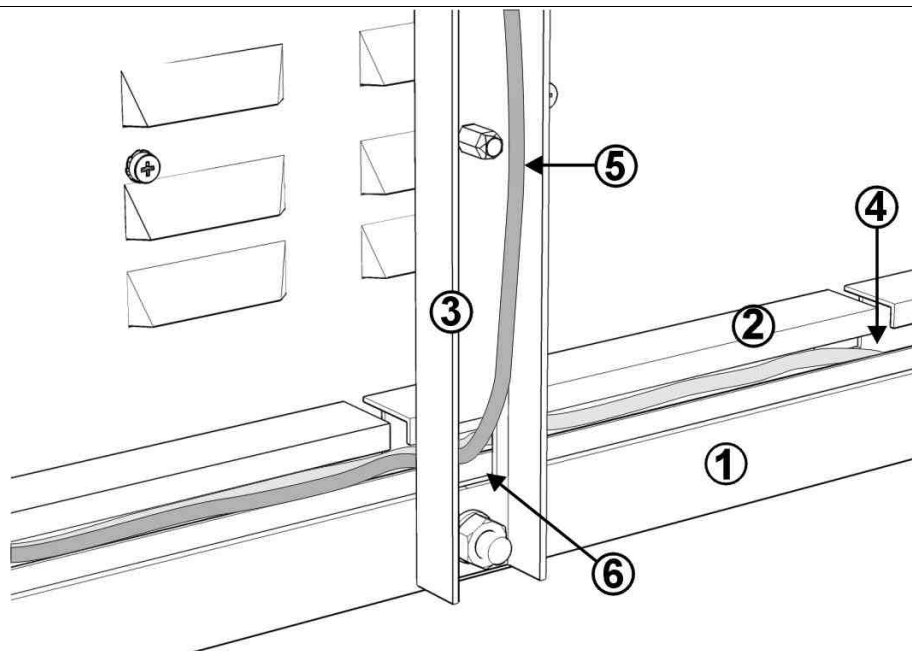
Inserimento dei cavi nelle canaline passacavi
